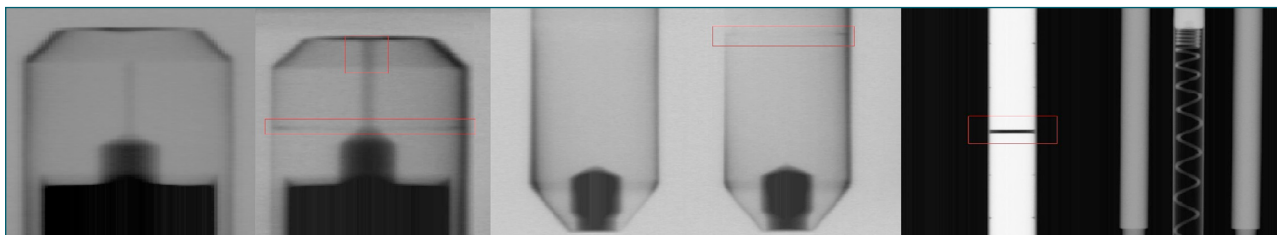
Ejemplos de placas radiográficas (de izda. a dcha.: tapón superior en barra PWR soldada y sellada; tapón superior en barra PWR sin sellar ni soldar, tapón inferior en barra PWR soldada, tapón inferior en barra PWR sin soldar, hueco en columna de pastillas, medida del plenum o muelle).
